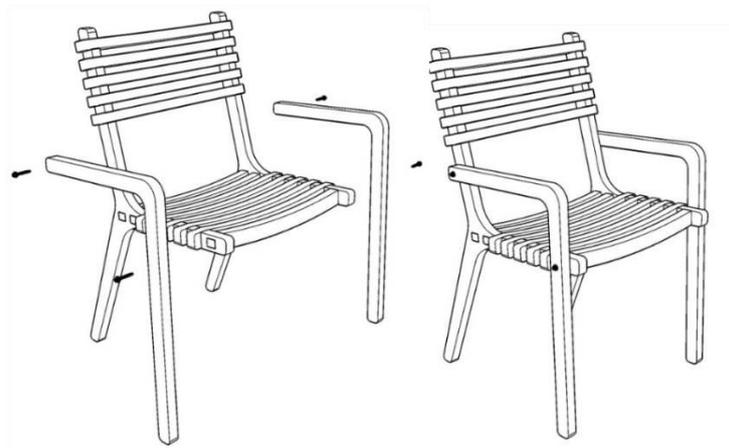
Demonstrativo do 4º passo; Fonte: Autora.
